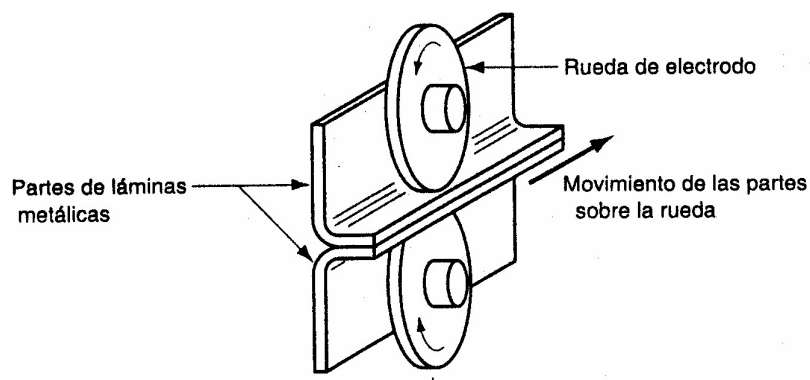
Soldadura de engargolado por resistencia (RSEW)
